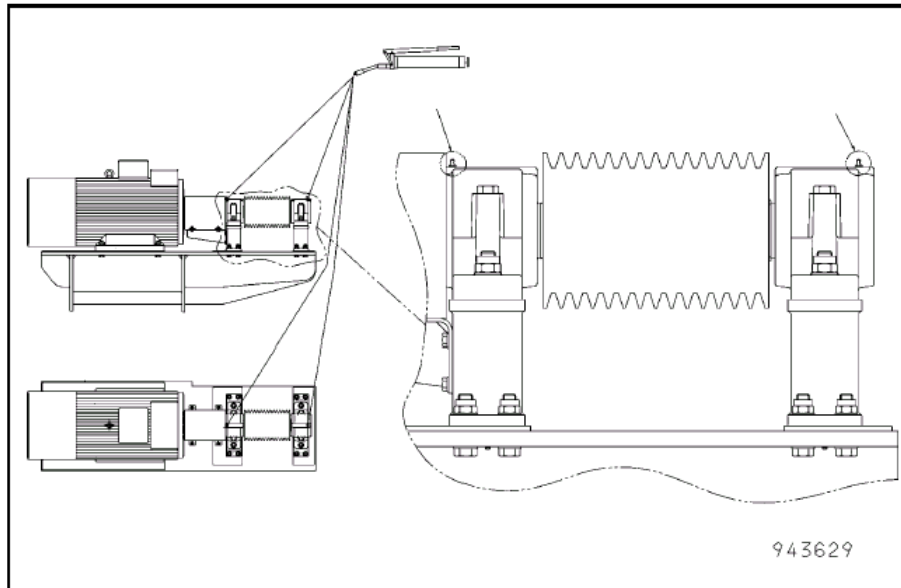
Схема последовательности смазки труднодоступных подшипников опорного вала
